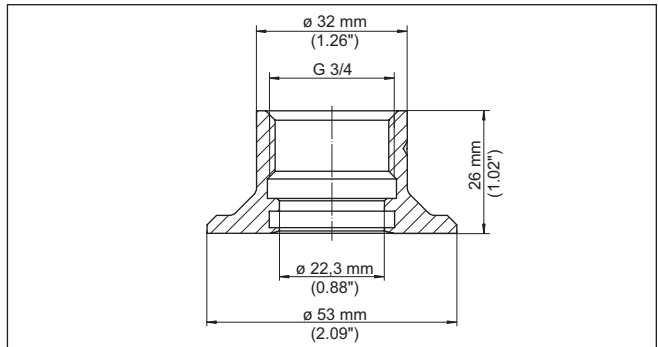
Maße Einschweißstutzen G $\frac{3}{4}$ (ISO 228-1)
